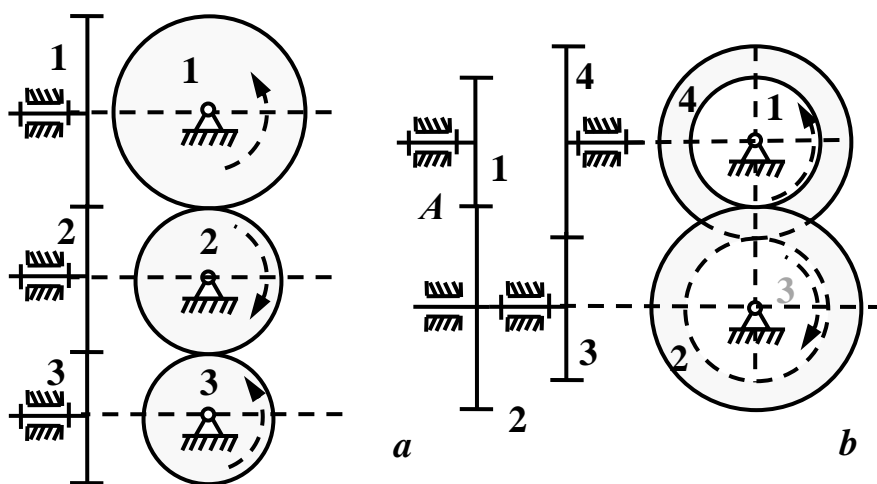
Рядовой (a) и ступенчатый (b) зубчатые механизмы
